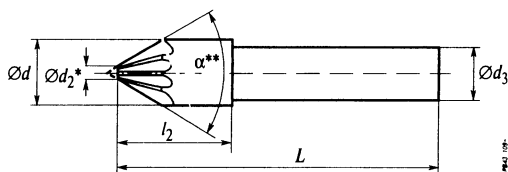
Размеры зенковки с цилиндрическим хвостовиком
